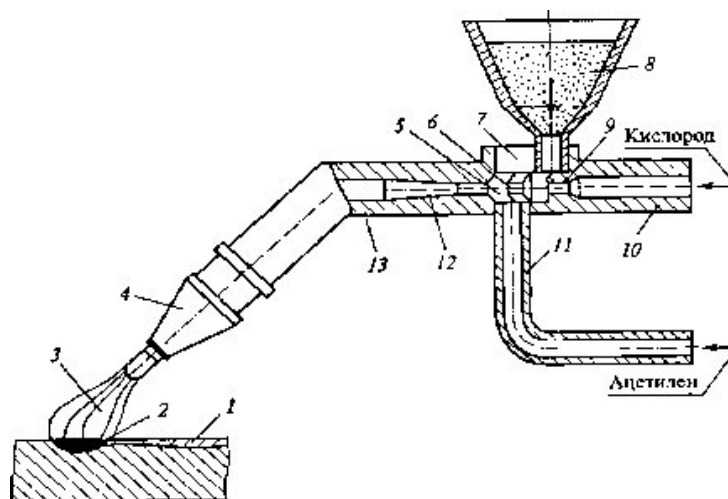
Установка, обладнана зварювальним пальником: 1 - наплавлена поверхня; 2 - зварювальна ванна; 3 - полум'я; 4 - мундштук; 5 - камера змішування; 6, 9 - інжектори; 7 - змішувальна камера; 8 - порошок; 10 - киснева трубка; 11 - ацетиленова трубка; 12 - канал; 13 - трубка
